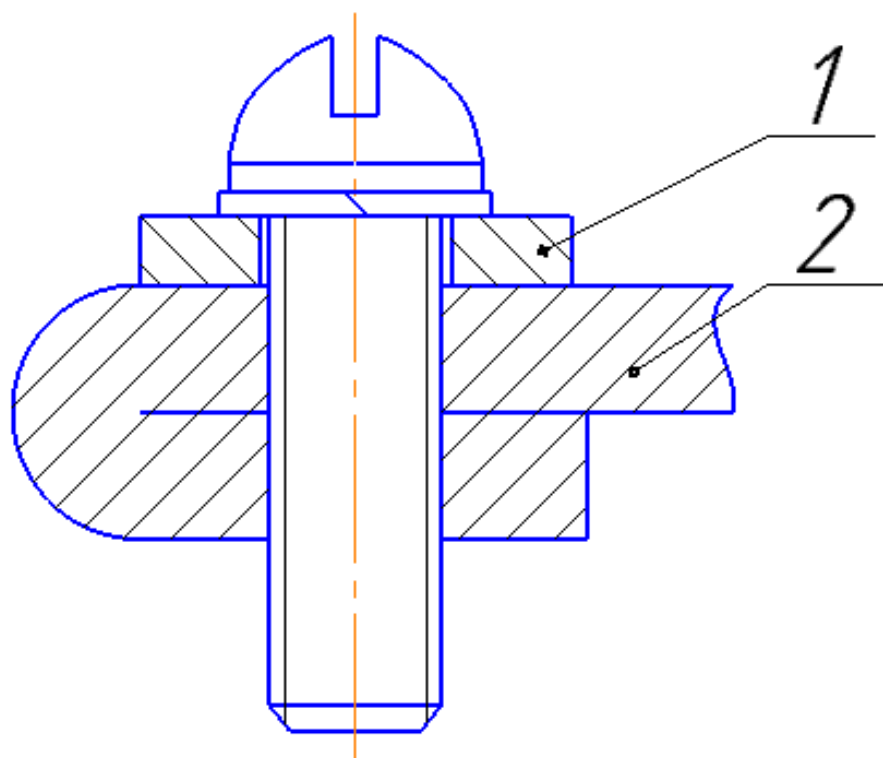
Увеличение длины резьбового отверстия за счет гибки листа: 1 – накладка; 2 – заготовка.
